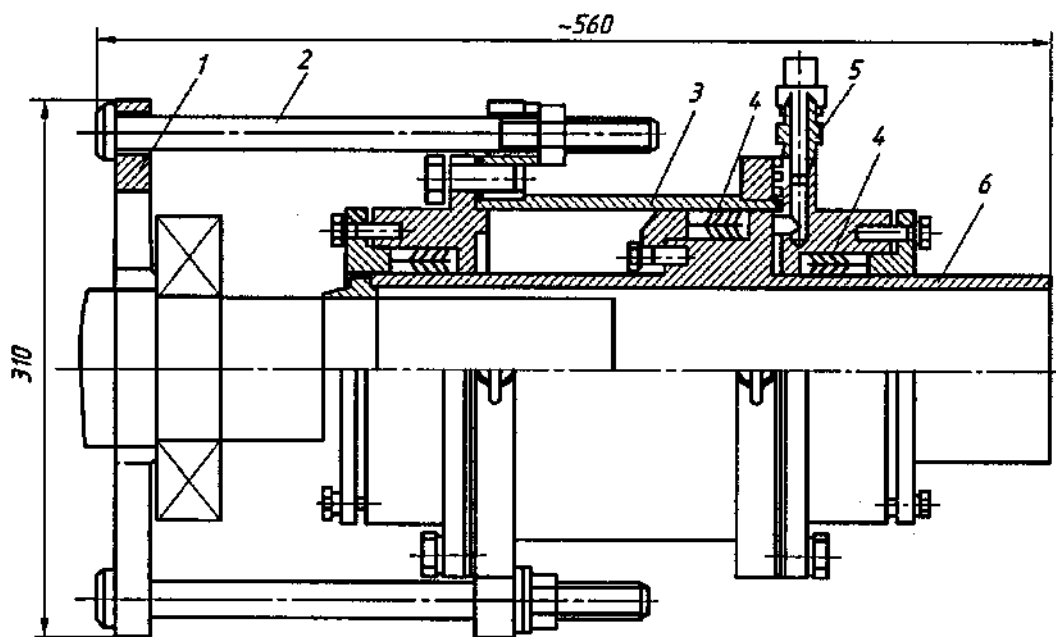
Гидравлический подвесной съемник для снятия подшипников с валов двигателей с высотой оси вращения 180–280 мм: 1 – скоба; 2 – тяга; 3 – цилиндр; 4 – уплотнение; 5 – штуцер; 6 – поршень
